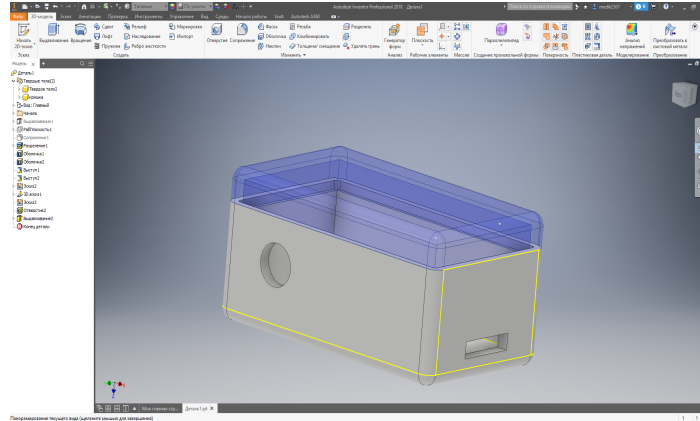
Прототип корпусу розроблений у Autodesk Inventor
